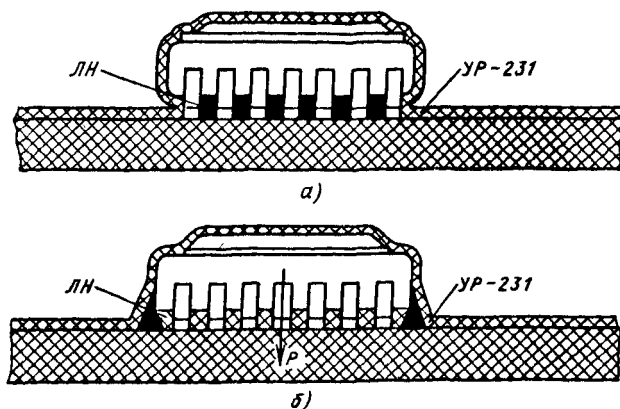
Правильная и неправильная установка планарного корпуса на печатную плату
